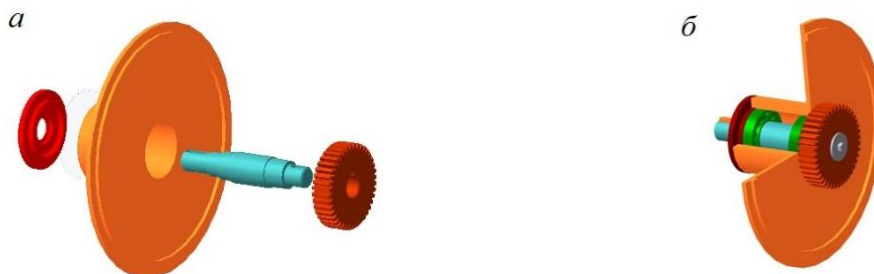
Моделі деталей: а – сонячного зубчастого колеса; б – їх зборка
